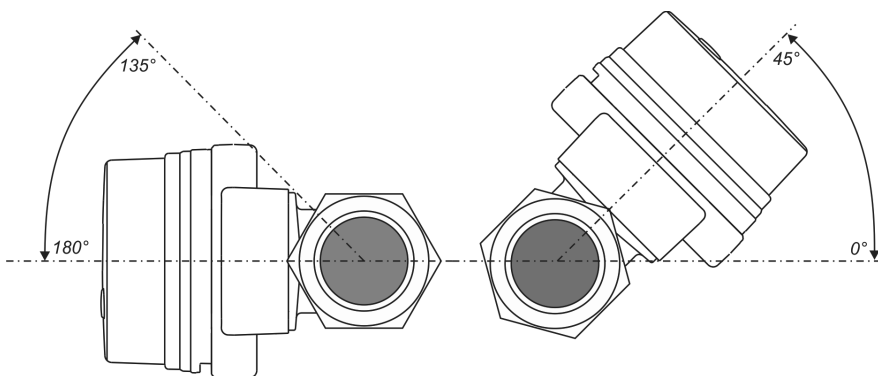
Рекомендуемая ориентация ЭБ расходомера при монтаже в горизонтальные и наклонные трубопроводы
